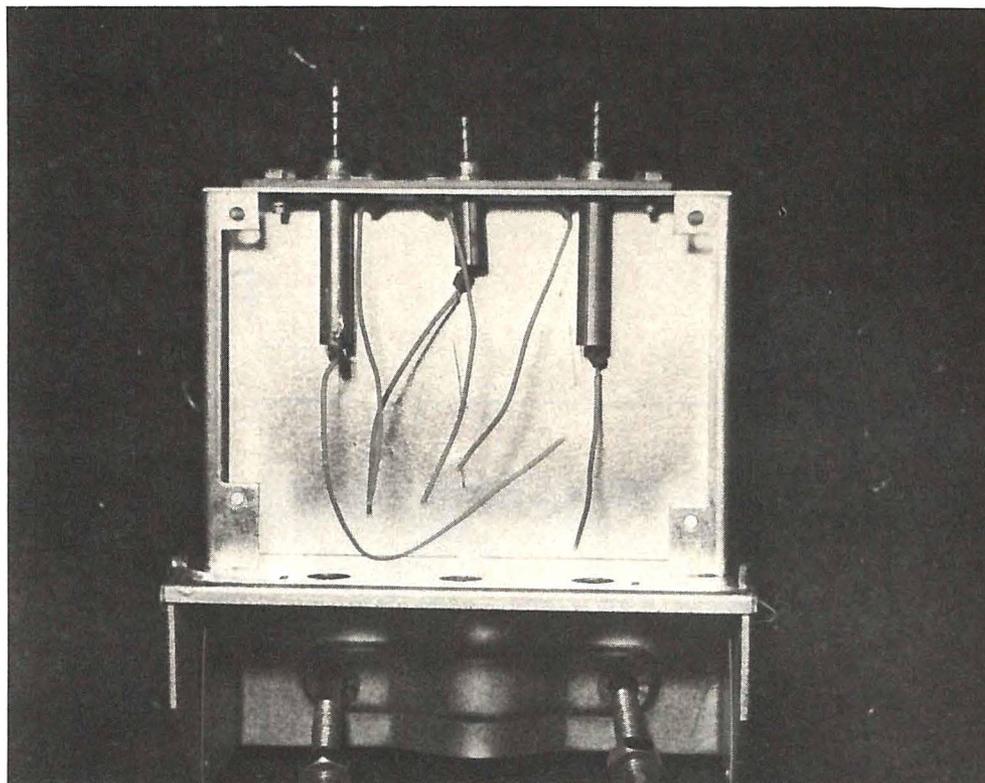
4 opération - soudage des fils de connexion
